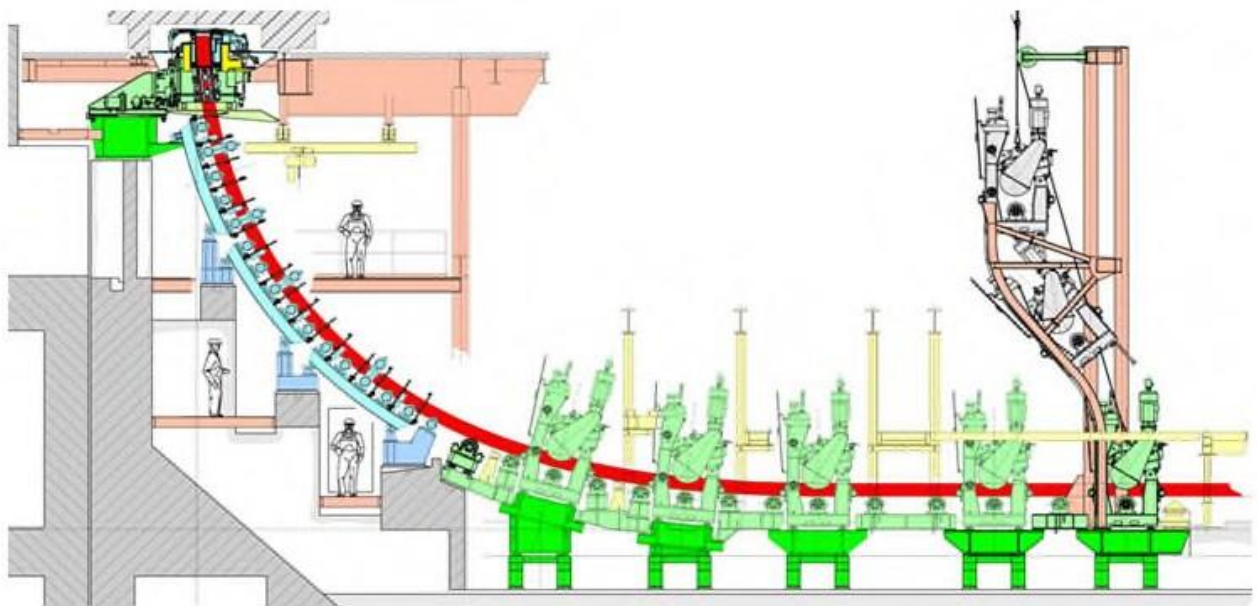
Схема радіальної машини безперервної розливки для отримання круглих заготовок
